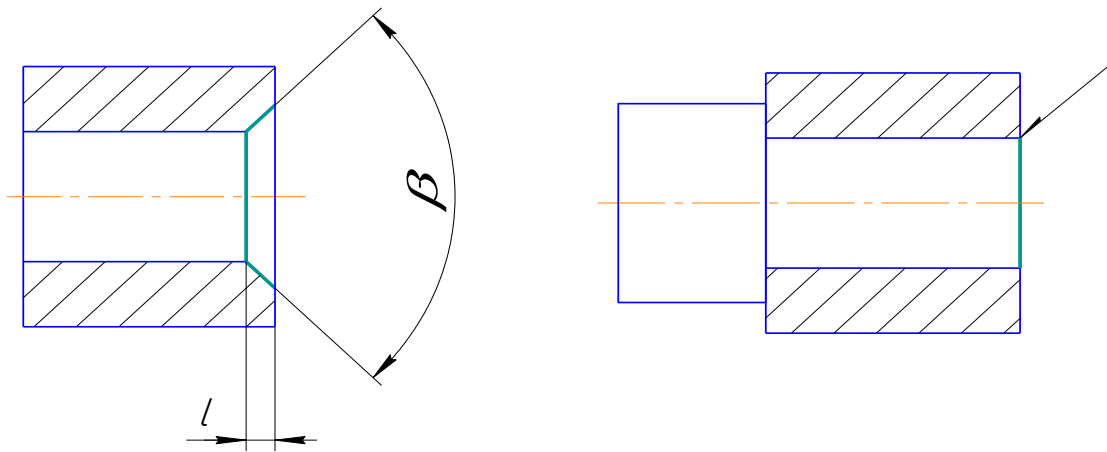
Приклад зображення на РК підготовки поверхні до зварювання, наплавлення, нанесення покриття
